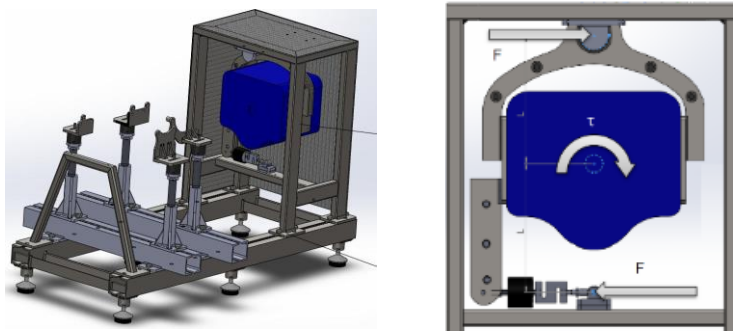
Diseño de la estructura para el banco dinamométrico y detalle del montaje colgante del retardador.
